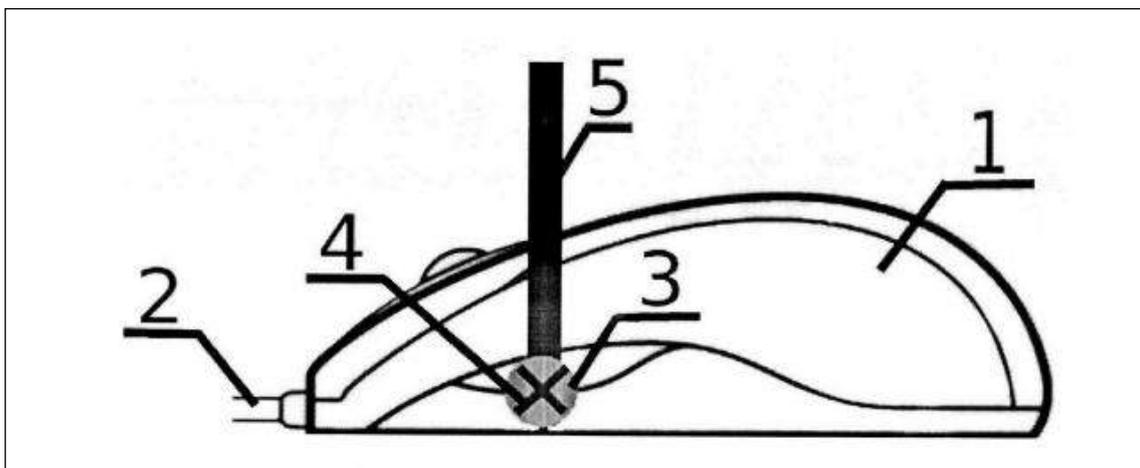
Чертеж тренажера-манипулятора для подготовки киберспортсменов
